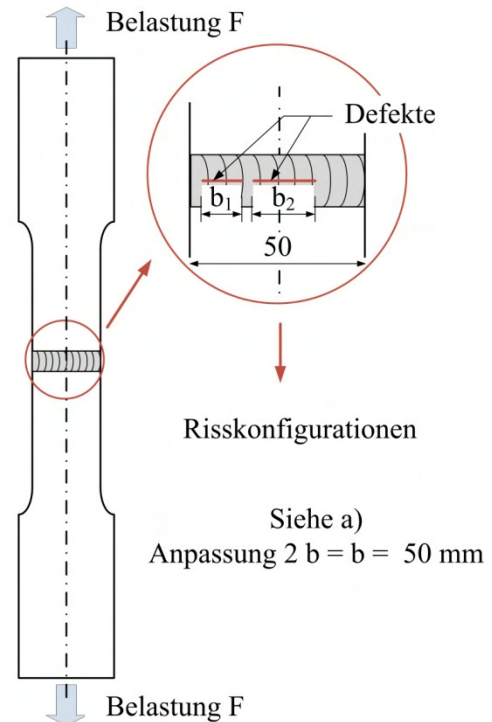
Lage des Defekts in der Schweißprobe sowie abgeleitete Risskonfiguration
